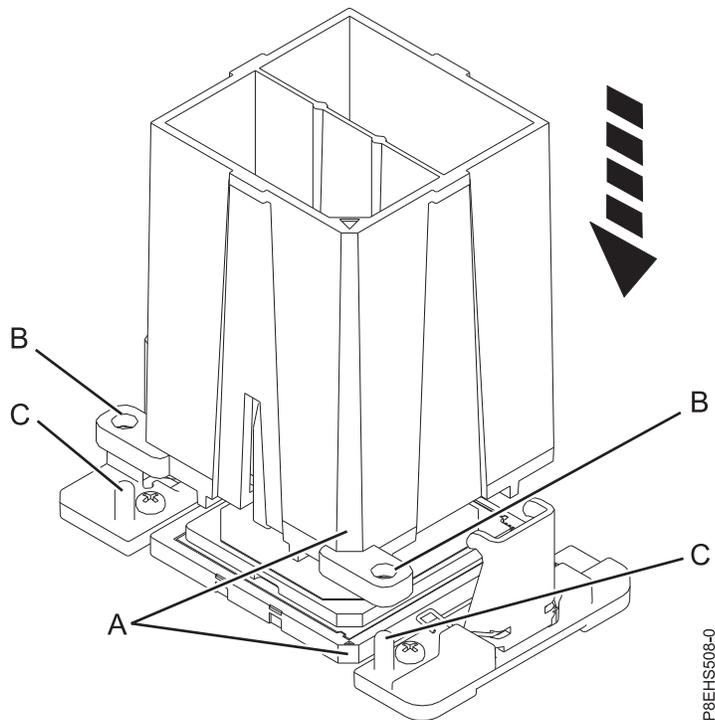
Ausbauwerkzeug auf das Systemprozessormodul herabsenken
